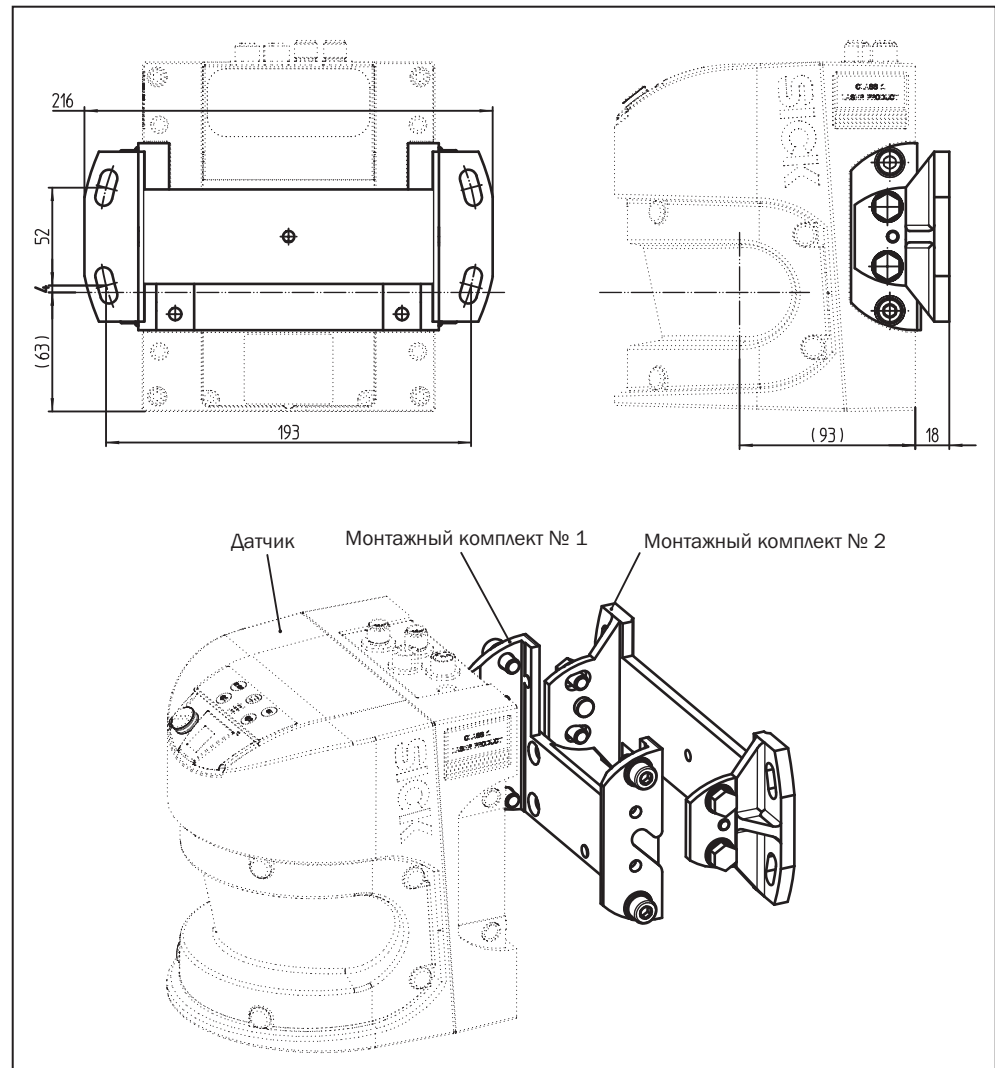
Размерный чертеж монтажного комплекта № 2 (мм)
